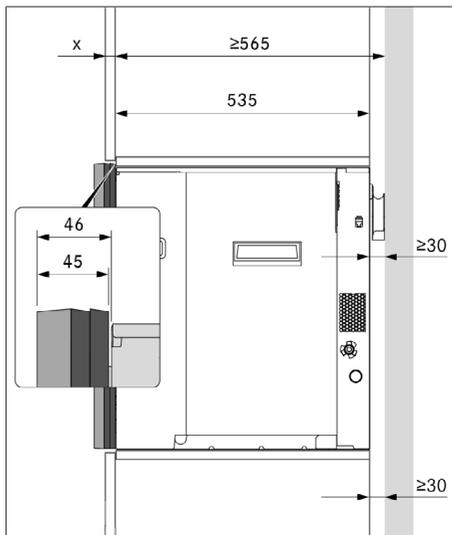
Dimensões de instalação com 2 estruturas de espaçamento
